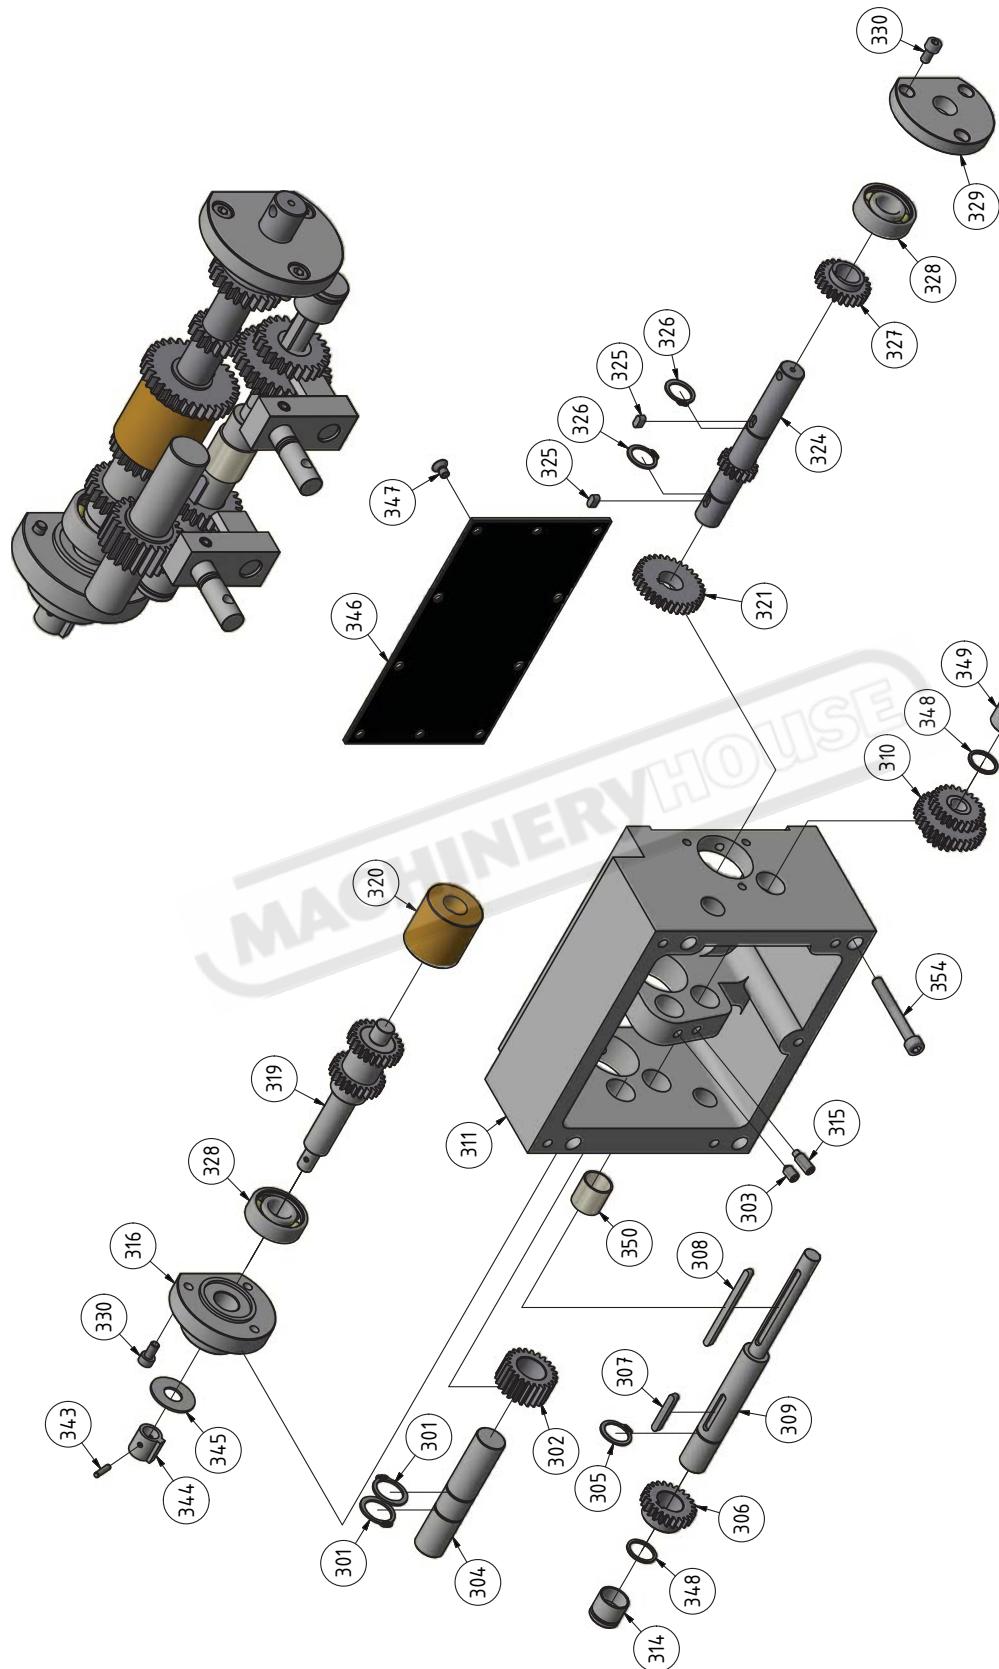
Vorschubgetriebe 2 von 2 - Feed gear 2 of 2 - TU 2807
